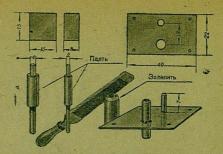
Деталь перфоратора: пластин-ка с пробойными трубочками.
